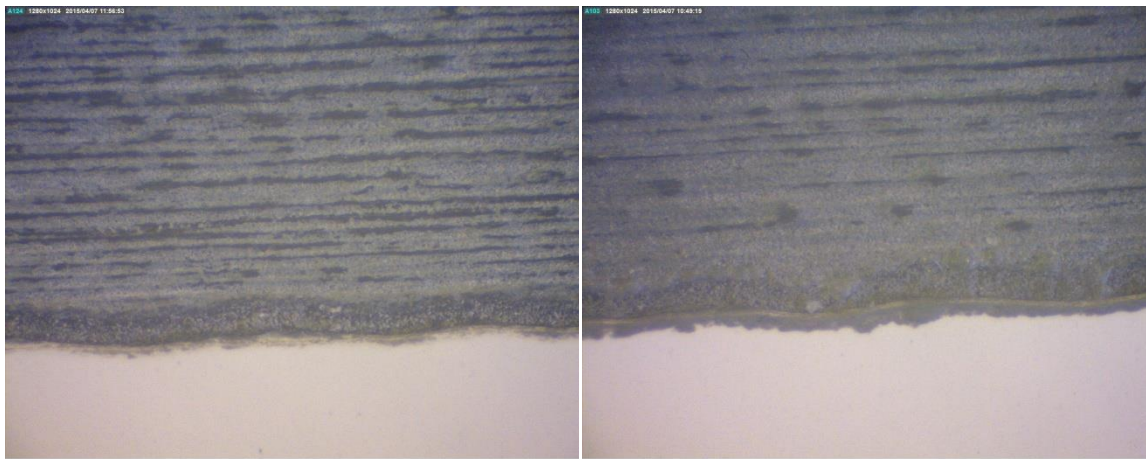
Experimentální obrábění vzorku Fólie - bílá
